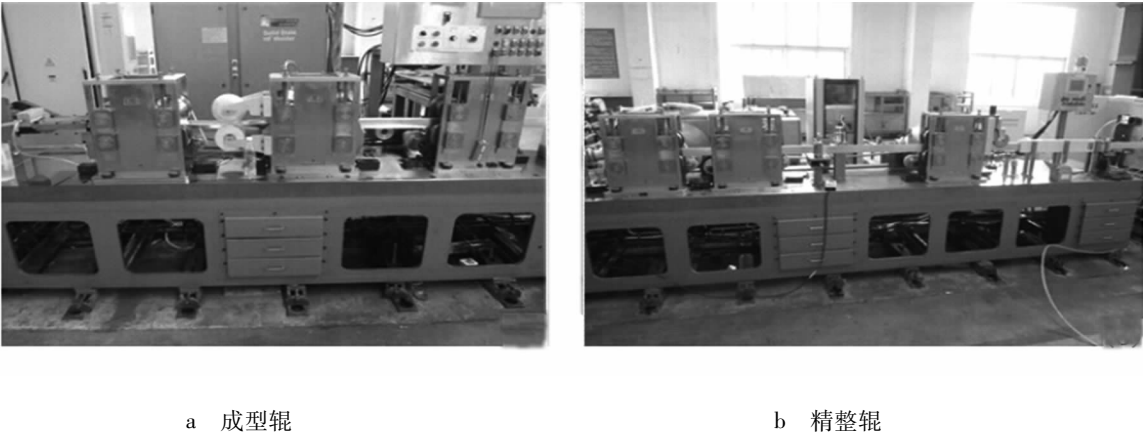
焊接前成型辊和焊接后精整辊实物图
